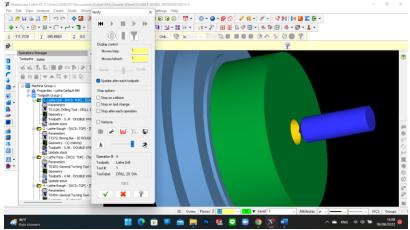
15 *Design* Awal Alur Pemesinan Pada MasterCAM Referensi 2D Drawing
